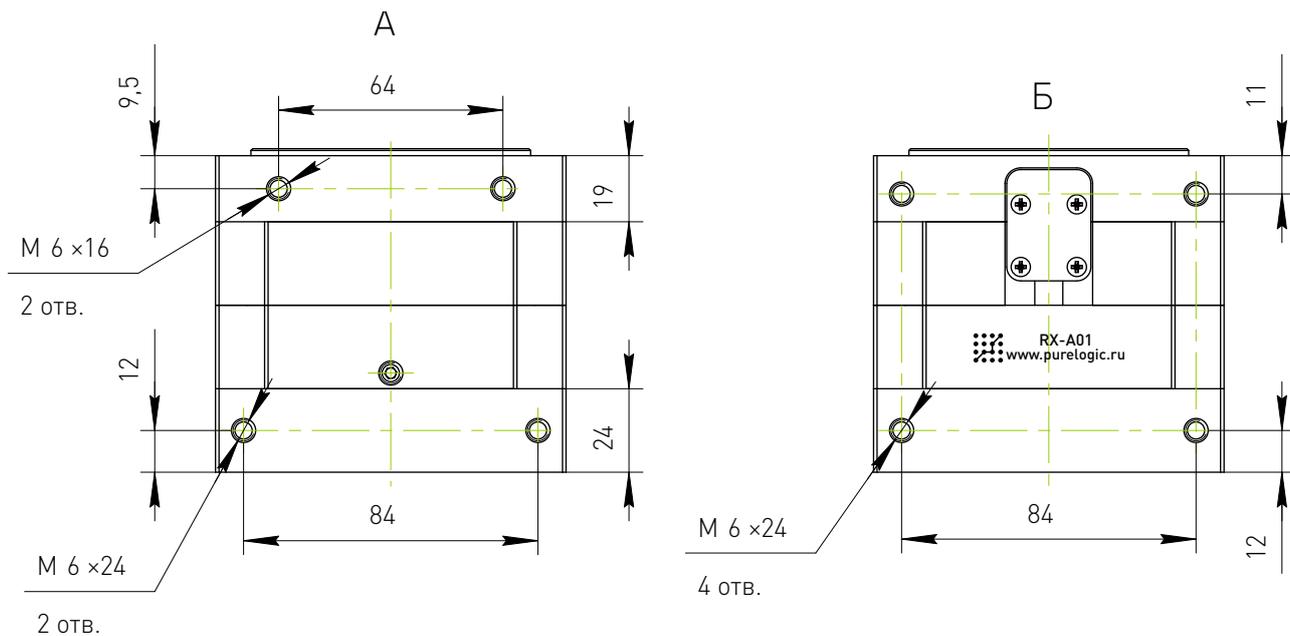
Габаритные и присоединительные размеры поворотной оси.
